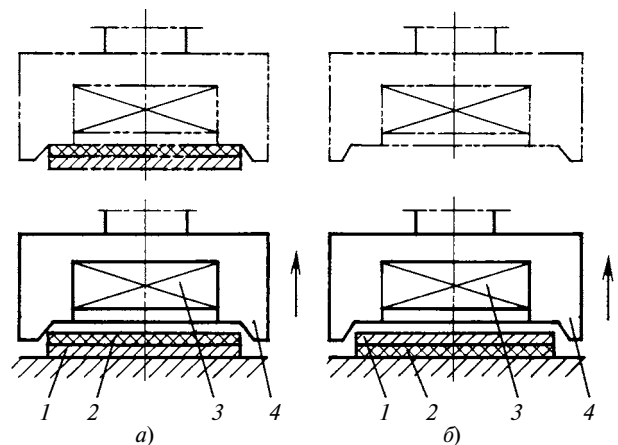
Схемы сортировки деталей с односторонним магнитным слоем с помощью селективного магнитного захвата:
